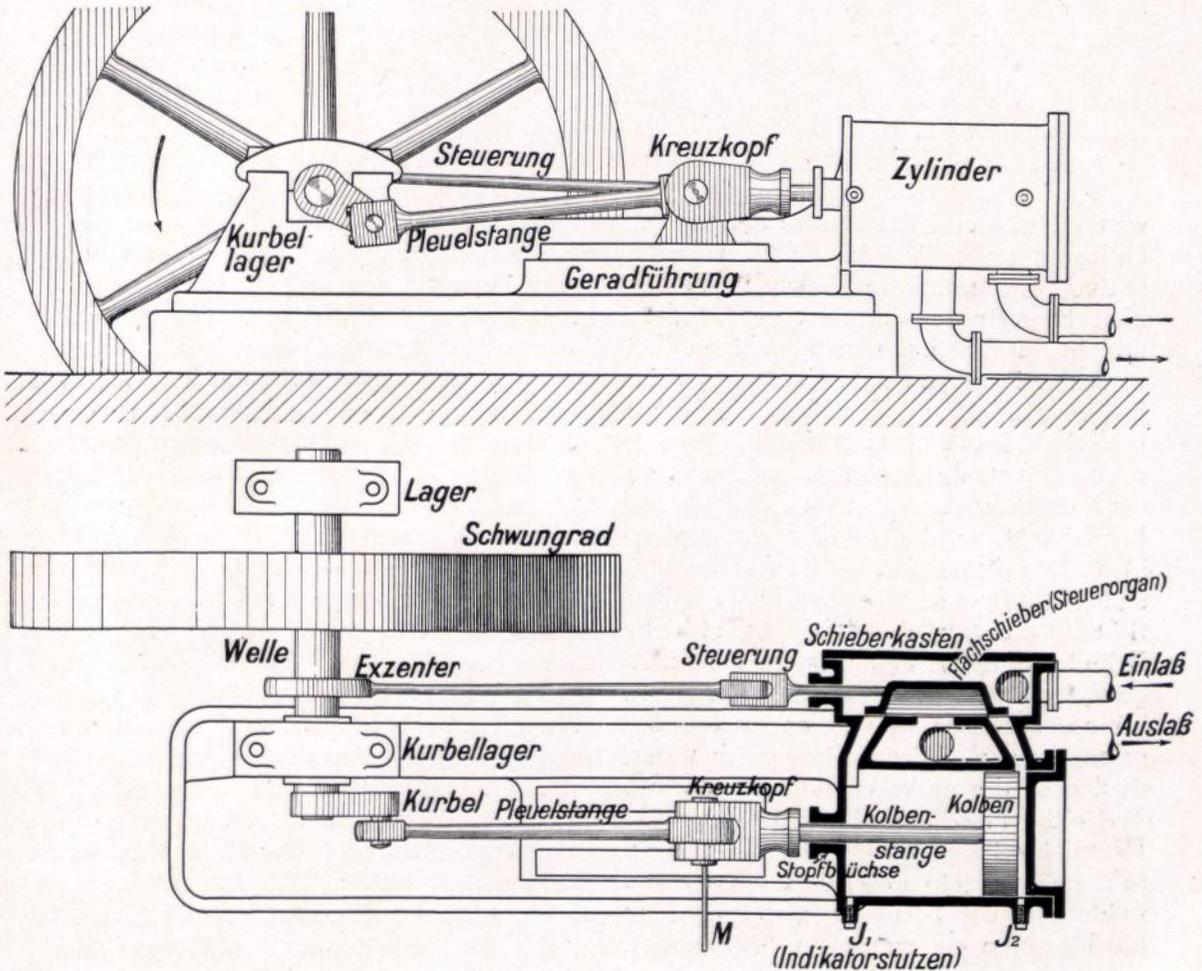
Schematischer Aufriß und Grundriß einer Kolbenkraftmaschine, mit (Druckwasser, Druckluft oder) Dampf zu betreiben. Im Grundriß ist der Zylinder geschnitten gedacht; die Schnittflächen sind geschwärzt. Die bewegten Teile sind — im Gegensatz zum Maschinengestell und Zylinder — durch Schattierung hervorgehoben.
